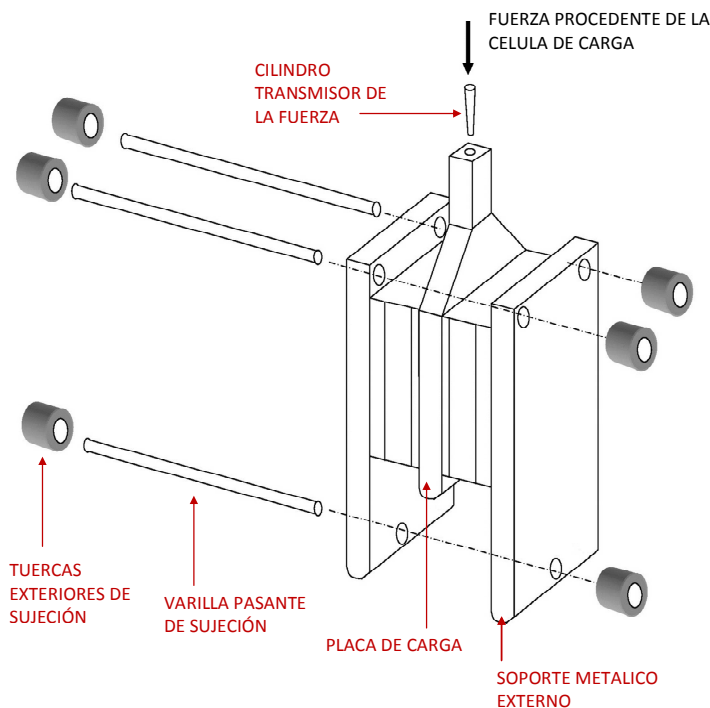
Ensayo de cortadura: utillaje diseñado y montaje del mismo
